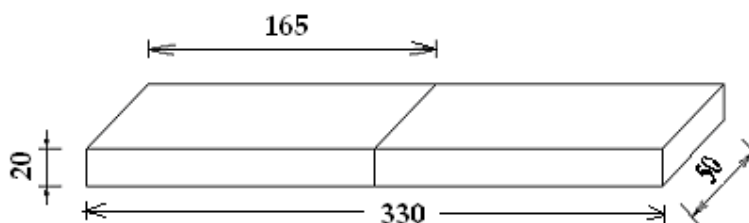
Geometria (em mm) utilizada para confecção dos corpos de prova das juntas encaixadas para o ensaio de tração.
